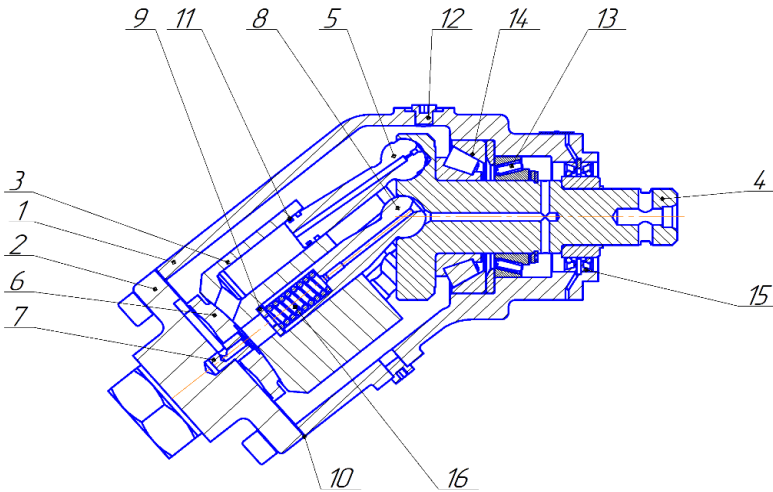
Аксиально-плунжерный насос: 1 – корпус; 2 – крышка; 3 – блок цилиндров; 4 – вал; 5 – плунжер; 6 – торцевой распределитель; 7 – штифт; 8 – сферическая часть оси; 9 – упор; 10 – уплотнение; 11 – уплотнение цилиндров плунжеров; 12 – заглушка; 13 – радиально-упорный подшипник; 14 – радиально-упорный подшипник
